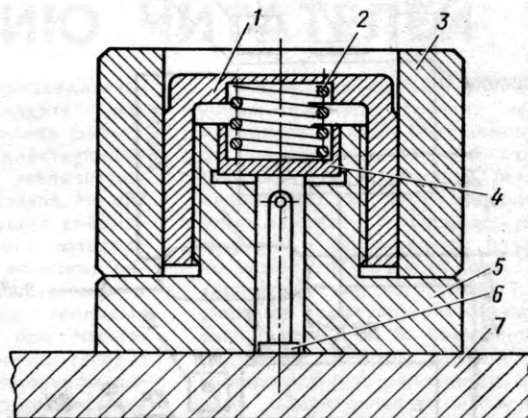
Приспособление для доводки торца корпуса распылителя: 1 — крышка; 2 — пружина; 3 — груз; 4 — втулка; 5 — корпус; 6 — корпус распылителя; 7 — плита доводочная
